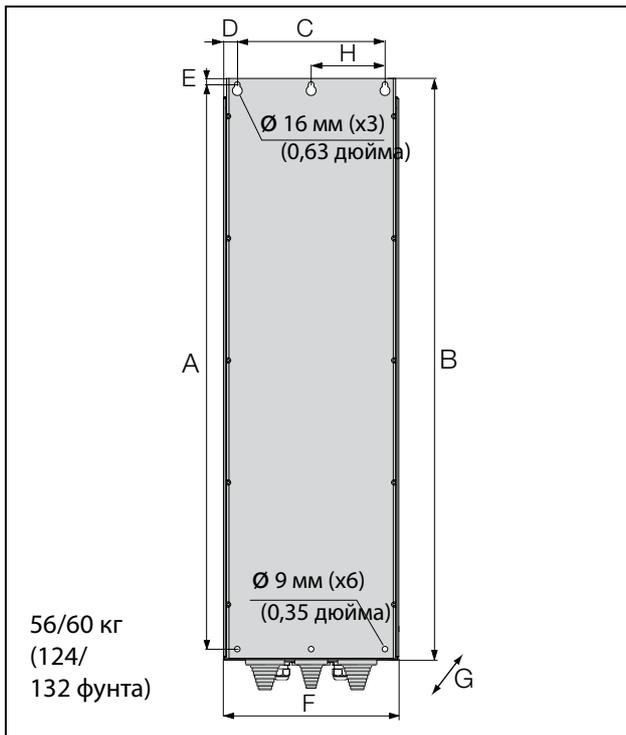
Устройство Emotron VFX моделей с 48-090 по 175 (размер корпуса E).
